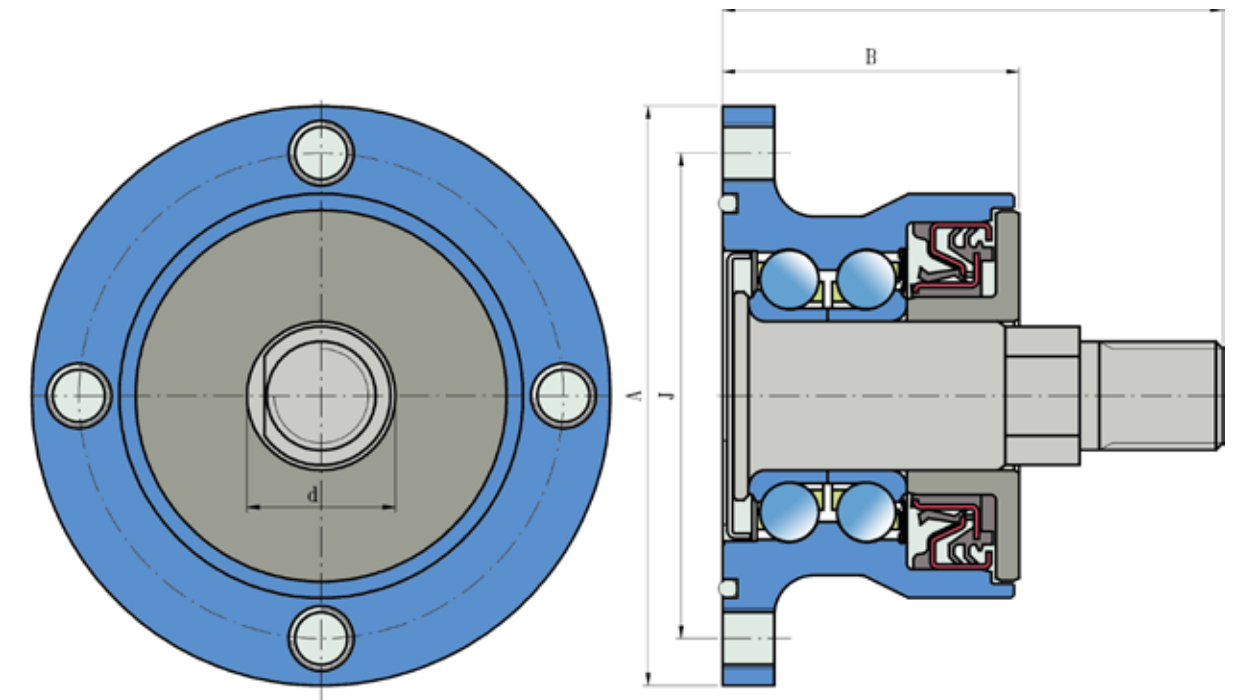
Технический чертёж подшипникового узла IL2-117-M22
